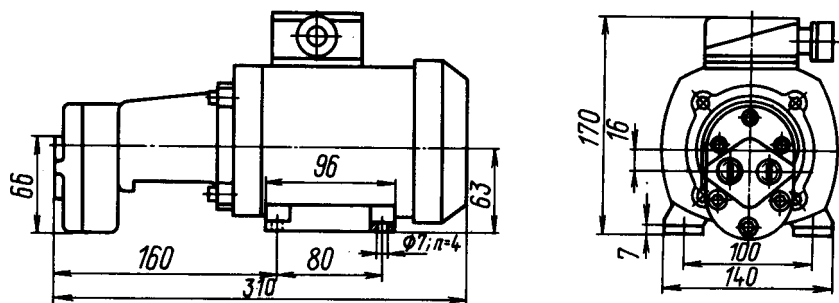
Габаритные и присоединительные размеры агрегата типа БГ11-1 с двигателем АИР63А4
